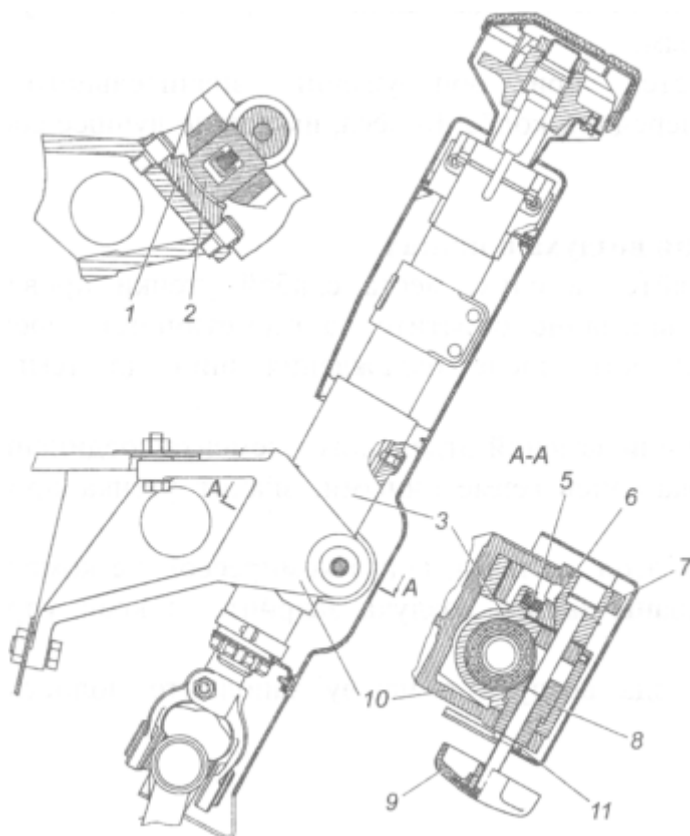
Рулевая колонка с механической регулировкой: 1 - рейка; 2 - сектор; 3 - колонка; 4, 5 - пружины; 6 - стопорное кольцо; 7, 8 - прижимы; 9 - маховичок; 10 - кронштейн; 11 - гайка.
